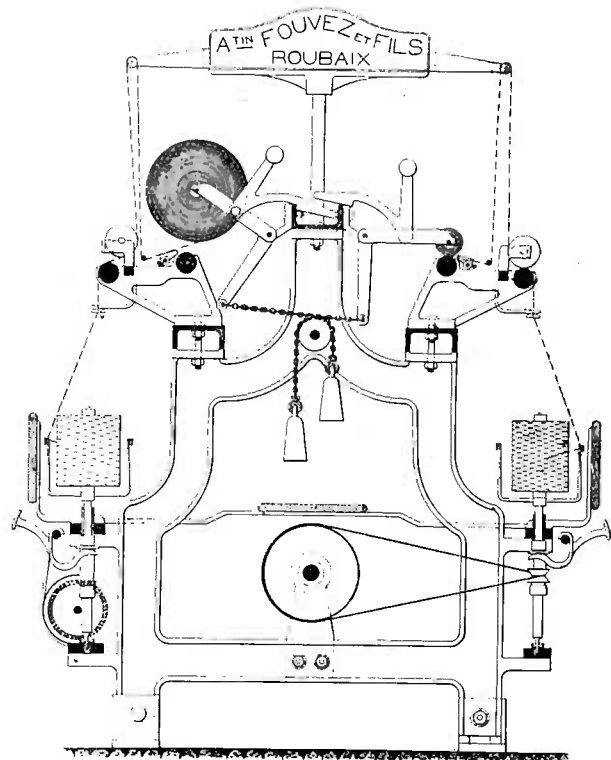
Retordeuse bobineuse. Construction Fouvez
